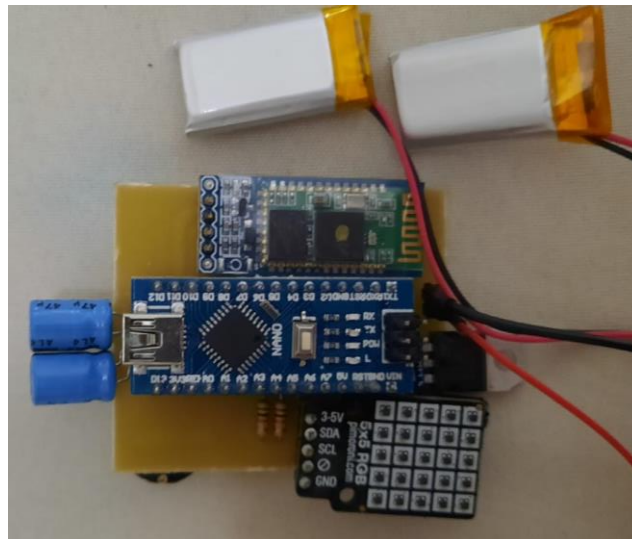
Vista real da parte superior da PCB com o Arduino, Bluetooth e Matriz de *Leds* soldados e as duas baterias de lítio-polímero ao lado
